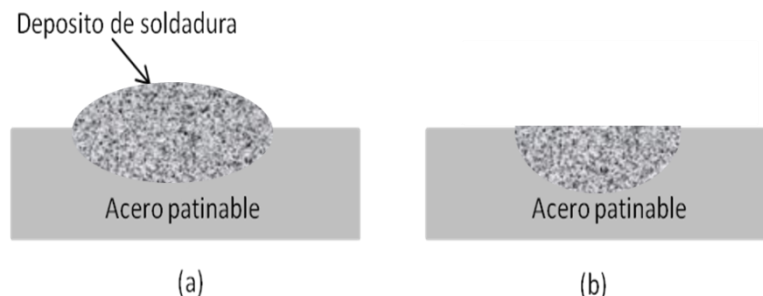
Probeta con depósitos de soldadura: sin rectificar (a) y rectificada (b).
